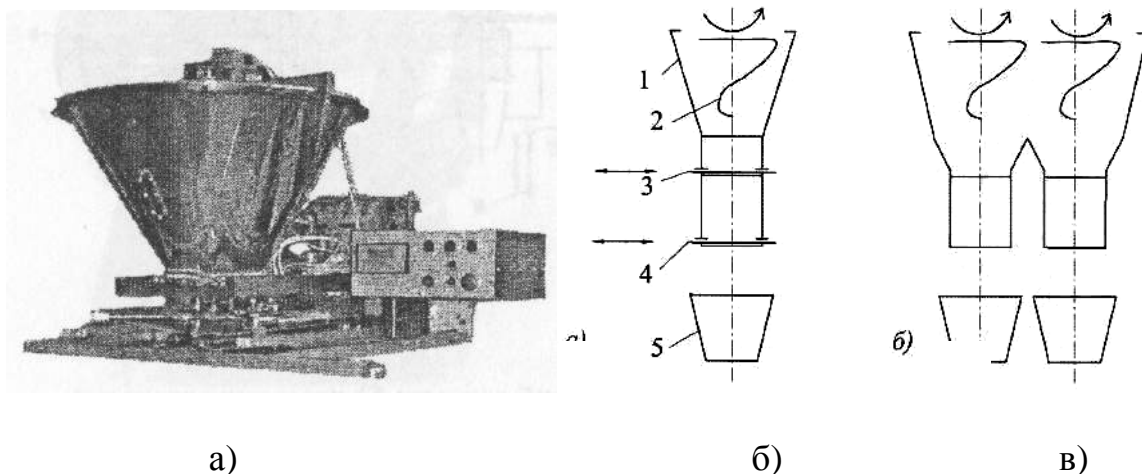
Дозатор шибєрного типу: а) загальний вигляд; б, в) схеми виконання шибєрного дозатора: 1 – бункер; 2 – мішалка; 3,4 – верхній і нижній шибєри; 5 – випускна воронка
